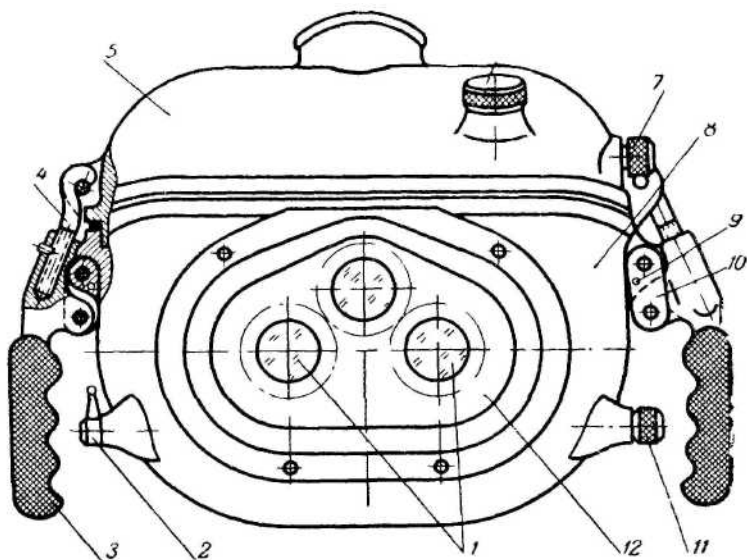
Внешний вид бокса для стереофотоаппарата «Спутник»: 1 — объективы; 2 — рычаг спуска; 3 — рукоятка транспортировки; 4 — крючок запора регулируемый; 5 — крышка бокса; 6 — маховик перемотки пленки; 7 — маховик наводки на резкость; 8 — корпус бокса; 9 — шплинт стопорный; 10 — щека шарнира запора; 11 — маховик регулировки диафрагмы; 12 — иллюминатор треугольный
